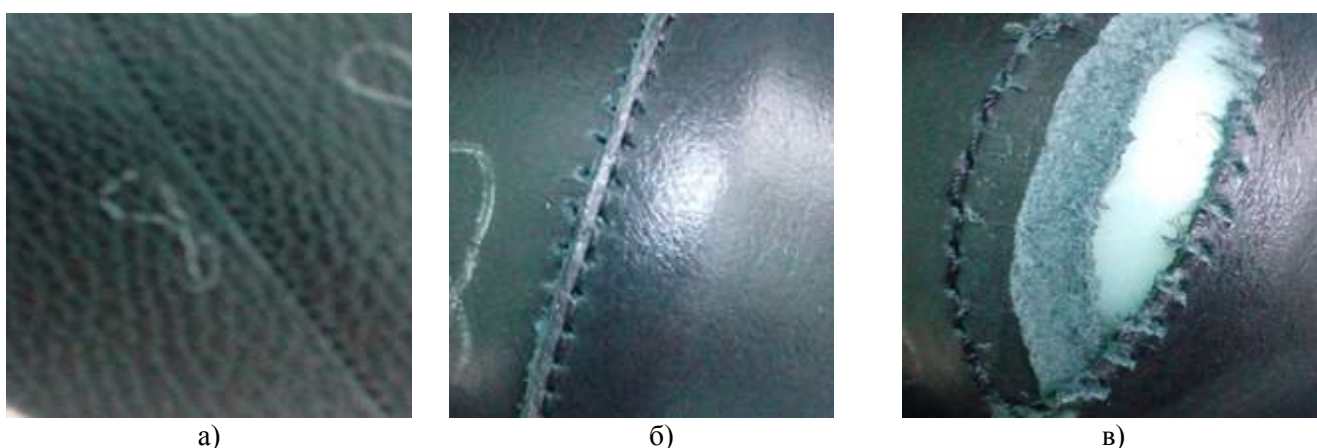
Внешний вид однорядного настрочного шва при сострачивании образцов (игла KKS, шов без упрочнения)
